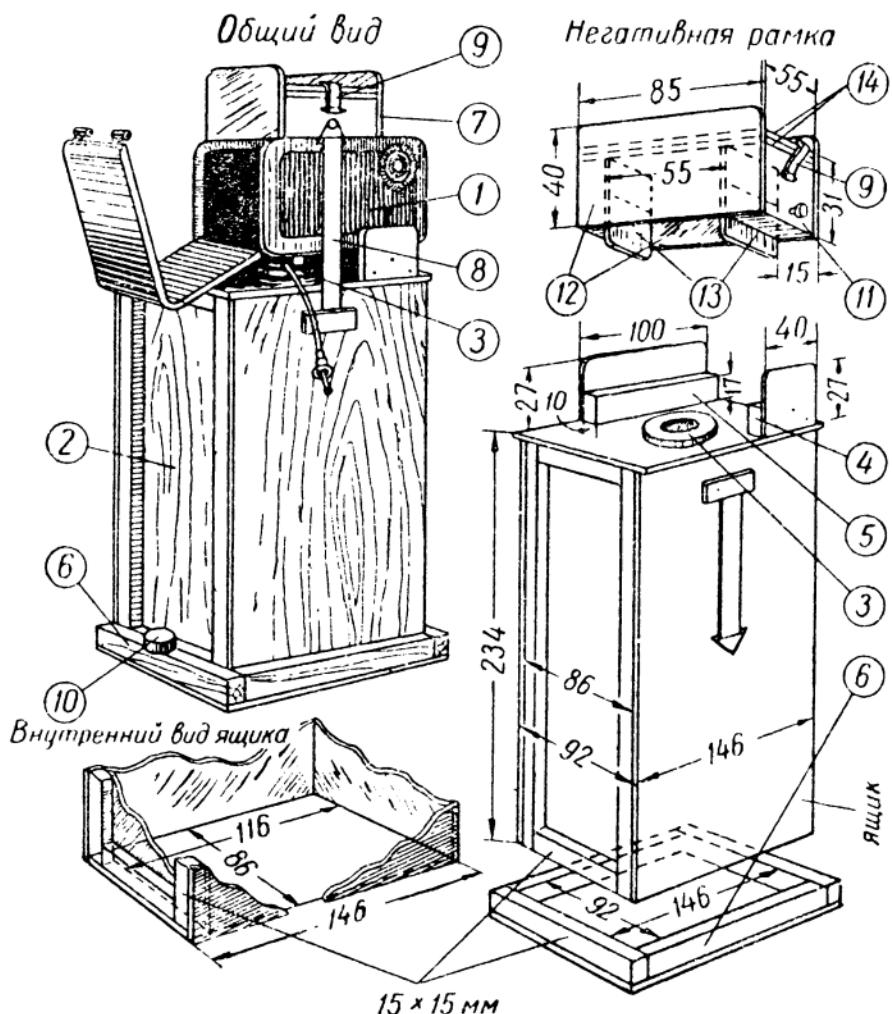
Схема устройства и размеры самодельной увеличительной приставки для фотоаппарата «Любитель»
